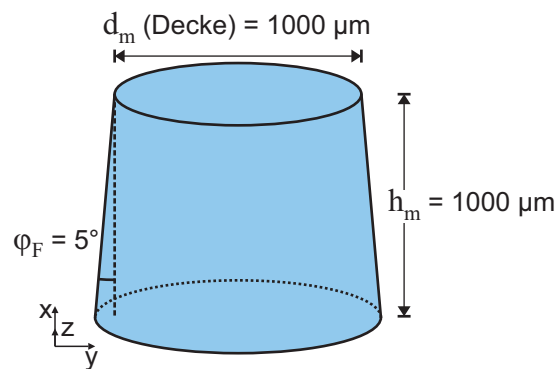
Zylindergeometrie angepasst für das Heißprägen. Die Höhe, der Durchmesser und der Flankenwinkel werden für eine gute Endformbarkeit vergrößert.
